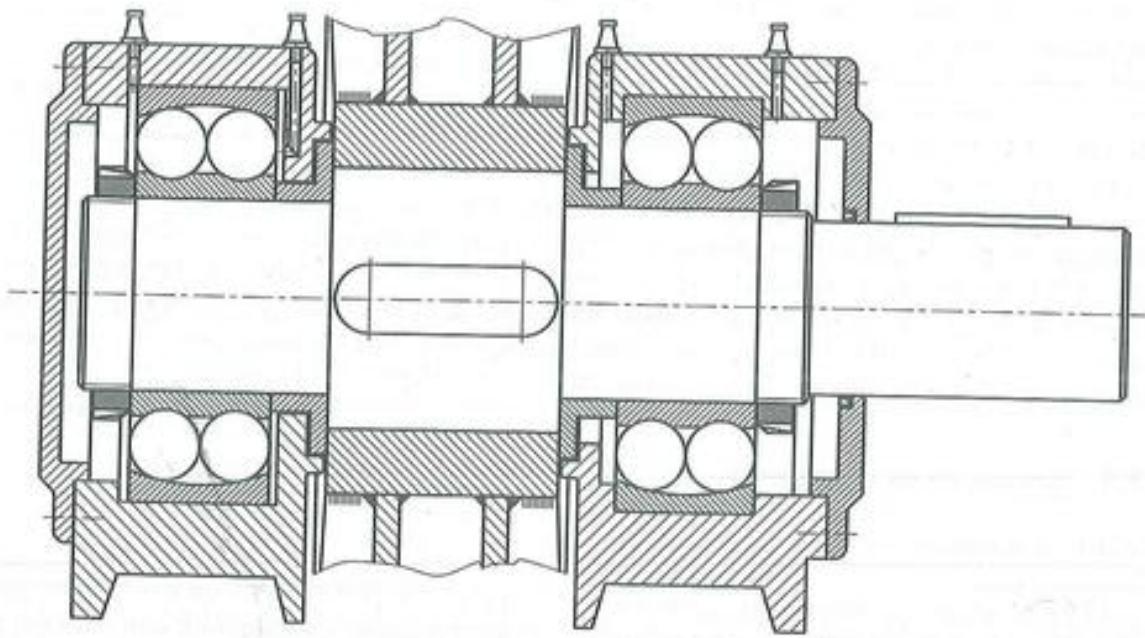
Disposición de rodamientos. Rodamientos de bolas a rótula. Rodamiento libre a la izquierda y rodamiento fijo a la derecha.
